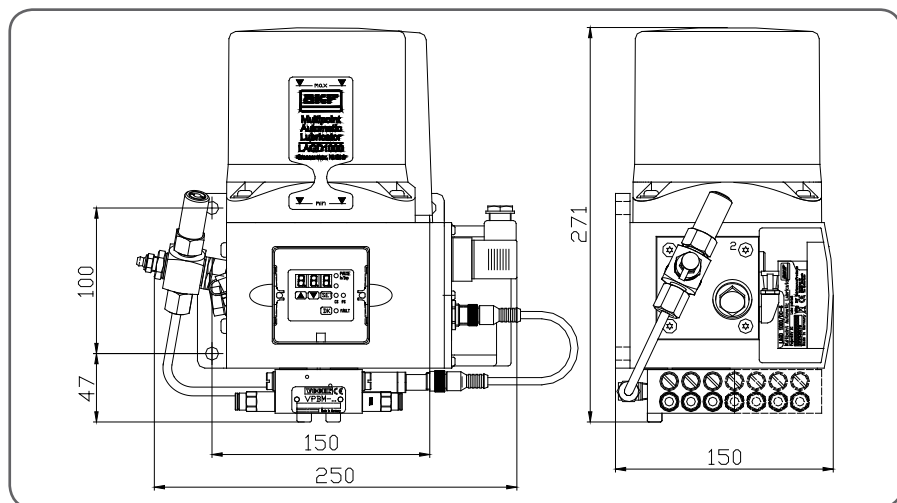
Габаритные размеры лубрикатора типа LAGD 1000/AC..
